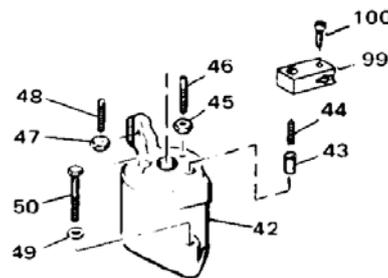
Покомпонентный чертеж регулировки цилиндра установки оборотов
